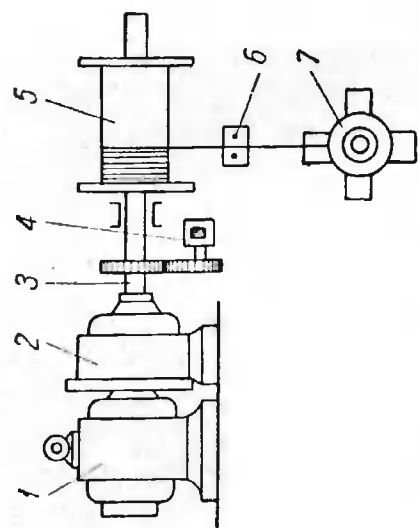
Малый намоточный станок с приводом от электродвигателя:
